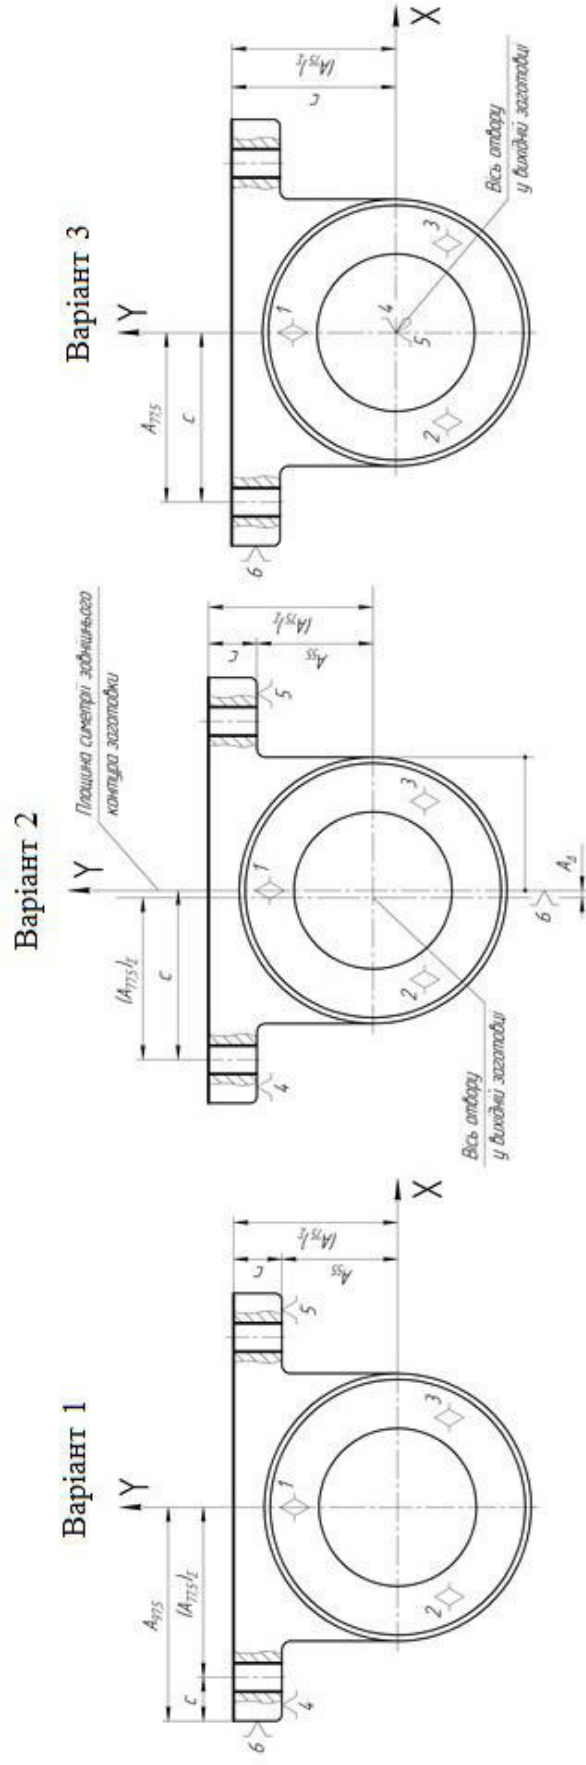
Варіанти схеми базування заготовки деталі типу «Корпус підшипника 420.008-01» на першій операції механічної обробки з технологічними розмірними ланцюгами для визначення похибки базування
